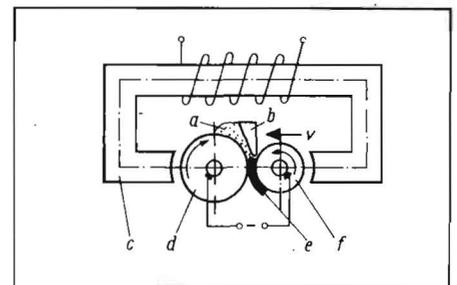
Schema des EIL-Verfahrens; a Magnetpulver, b Dosiereinrichtung, c Elektromagnet, d diamagnetisches Werkzeug, e Auftragschicht, f Werkstück
